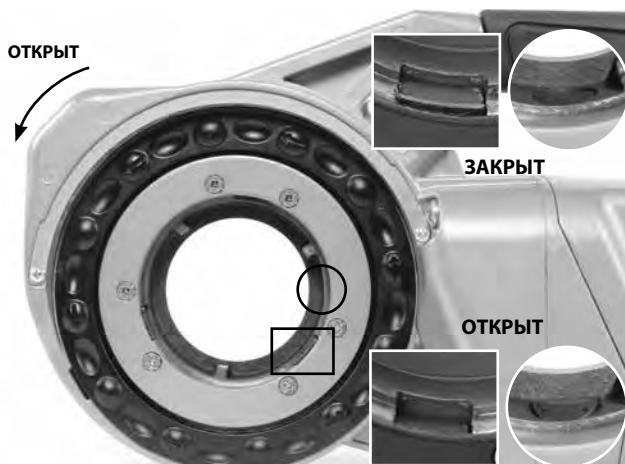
B - Стопорный механизм (760 FXP 11-R)
